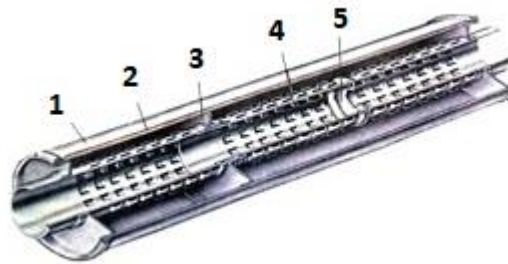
Резонатор: 1 – корпус; 2 – теплоізоляція; 3 – глуха перегородка; 4 – перфорована труба; 5 – дросель
